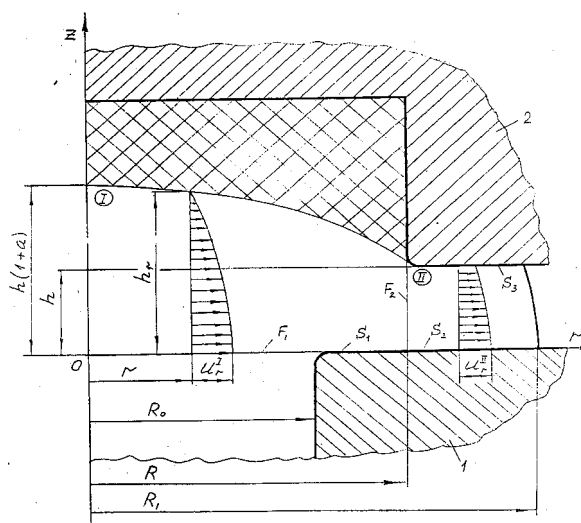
Схема течения металла на конечном этапе штамповки головки с фланцем
